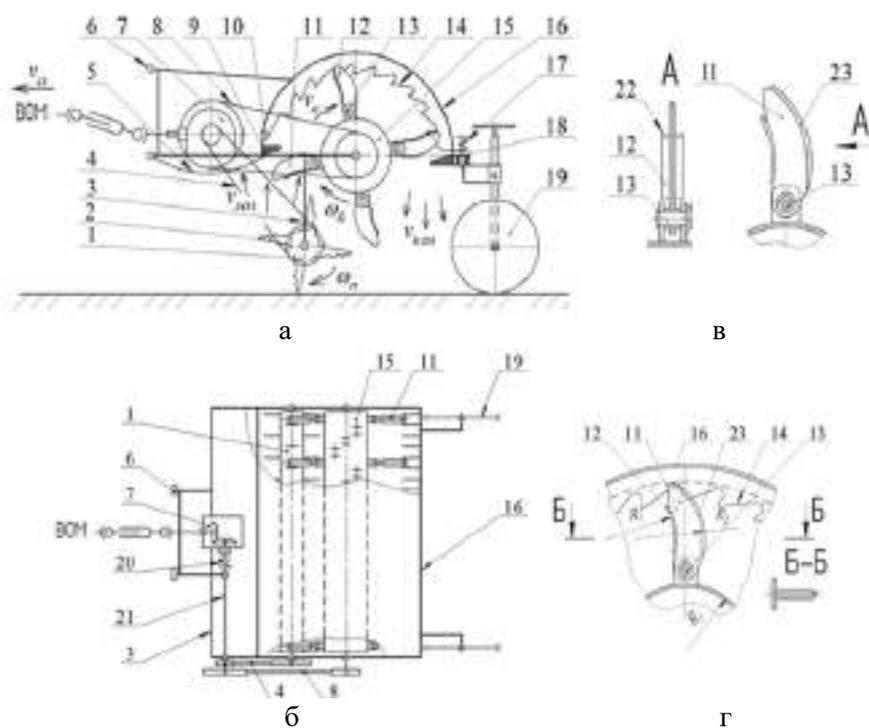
Схема конструктивная подборщика-измельчителя обрезков виноградной лозы: а – вид сбоку, б – вид сверху,
